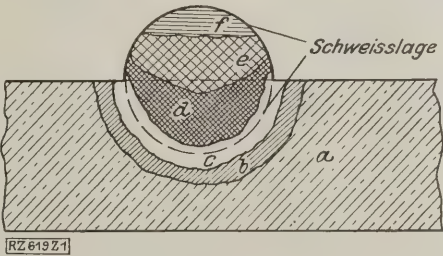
Schematische Darstellung des Aufbaues einer Kaltschweißung.
